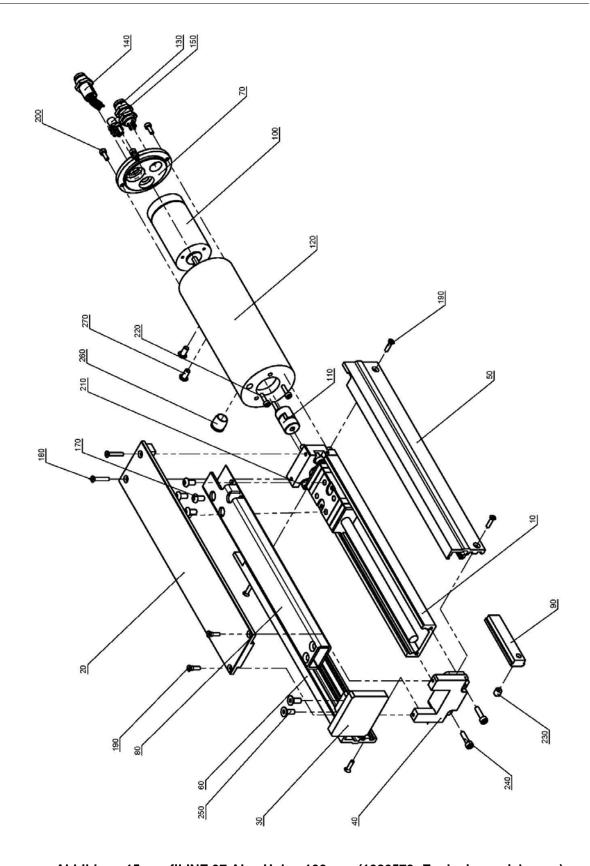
profiLINE 37 AL – Hub = 100 mm (1086573; Explosionszeichnung)
